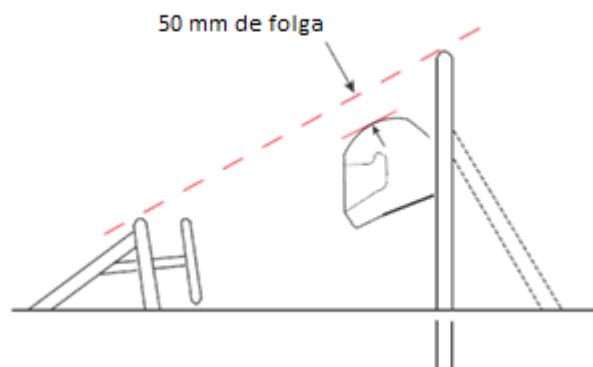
Envelope de segurança para cabeça do piloto. [7]
